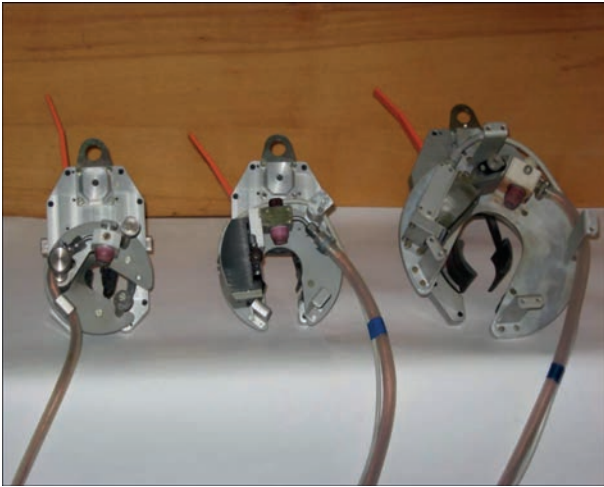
Общий вид головок сварочных АДЦ 627.03.00.000, АДЦ 625.03.00.000 и АДЦ 626.03.00.000 со стороны их планшайб
